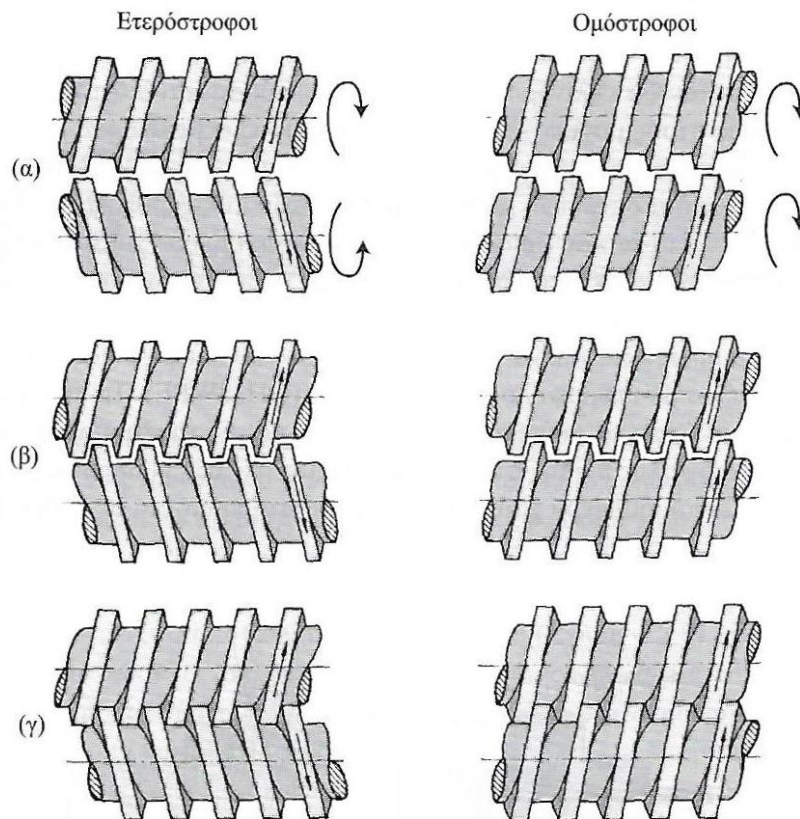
Ο διπλοκόγλιος εκβολέας της Welding Engineers [3].
